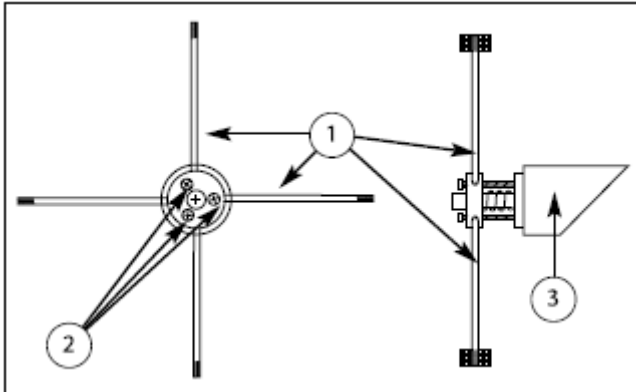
Assemblage du miroir secondaire (vue avant et latérale).
